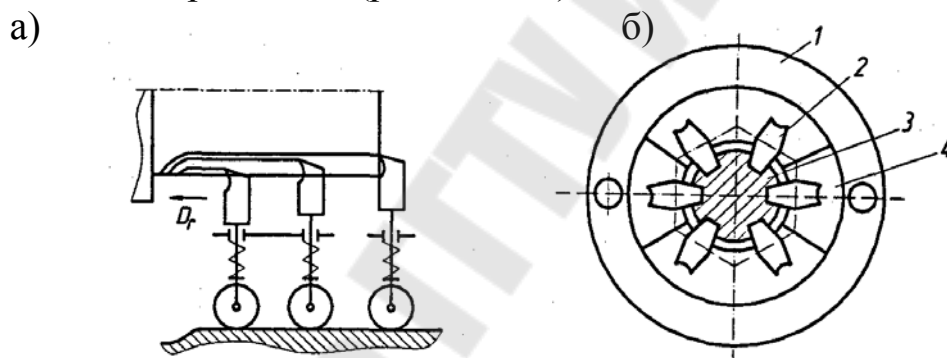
Схема шлицепротягивания (а) и накатной головки для шлиценакатного станка (б) (1 – корпус; 2 – накатной ролик; 3 – обрабатываемая деталь; 4 - сегмент)
